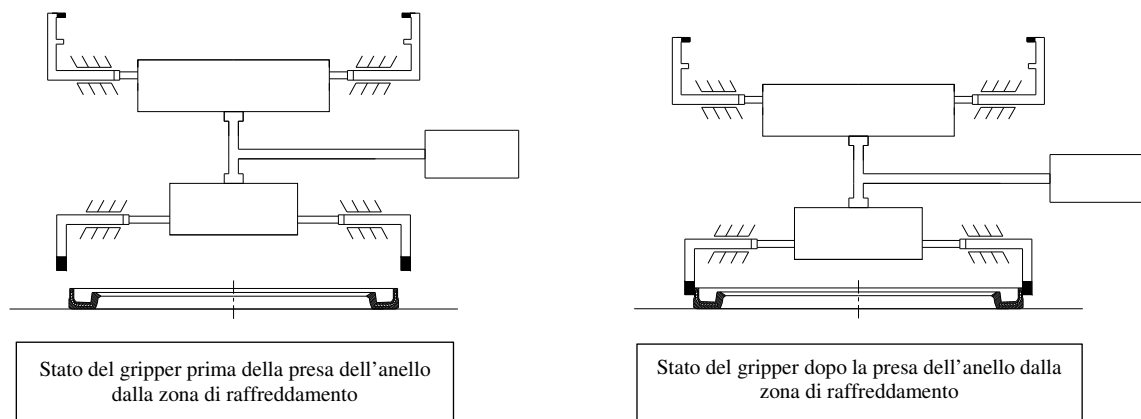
Fase di lavoro – Presa dell’anello dalla zona di raffreddamento.
